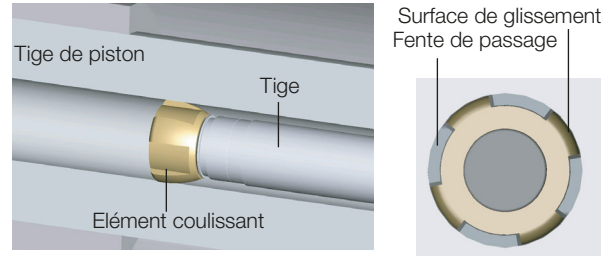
Vue détaillée et vue de dessus de l'élément coulissant
